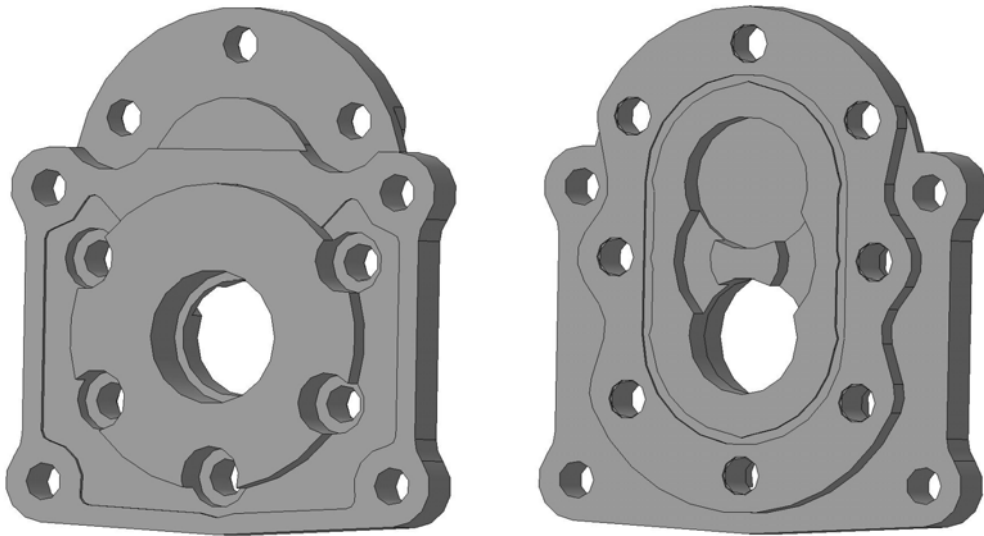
3D-модель виливка деталі «Кришка насоса НШ32.У» при литті в кокіль
